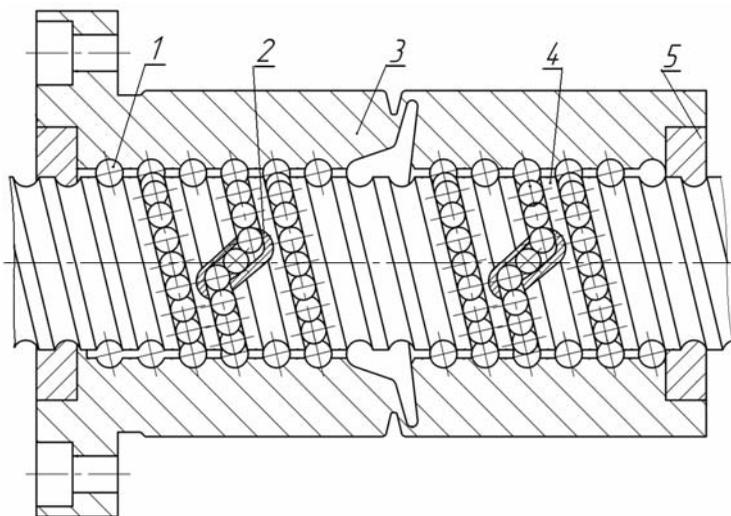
Передача винт-гайка качения с одной гайкой 3 с упругой перемычкой для регулирования натяга и с осевым упругим смещением обеих частей гайки
